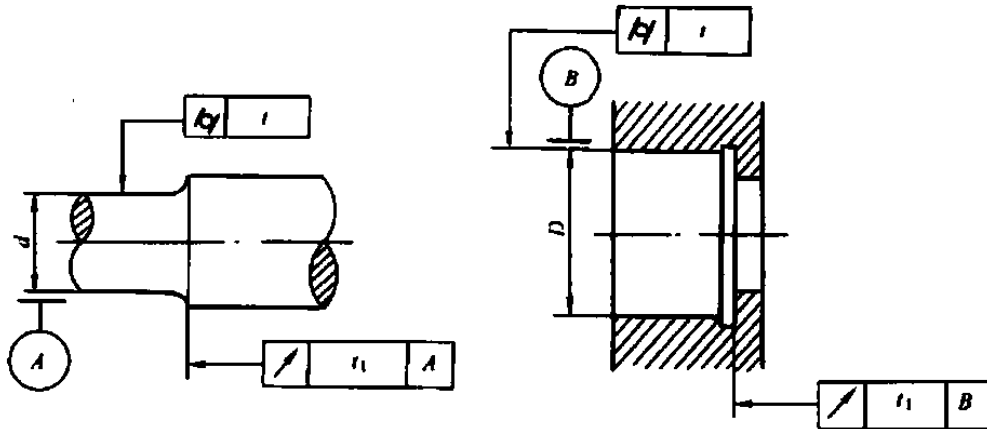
轴与外壳孔配合表面及端面的形位公差
